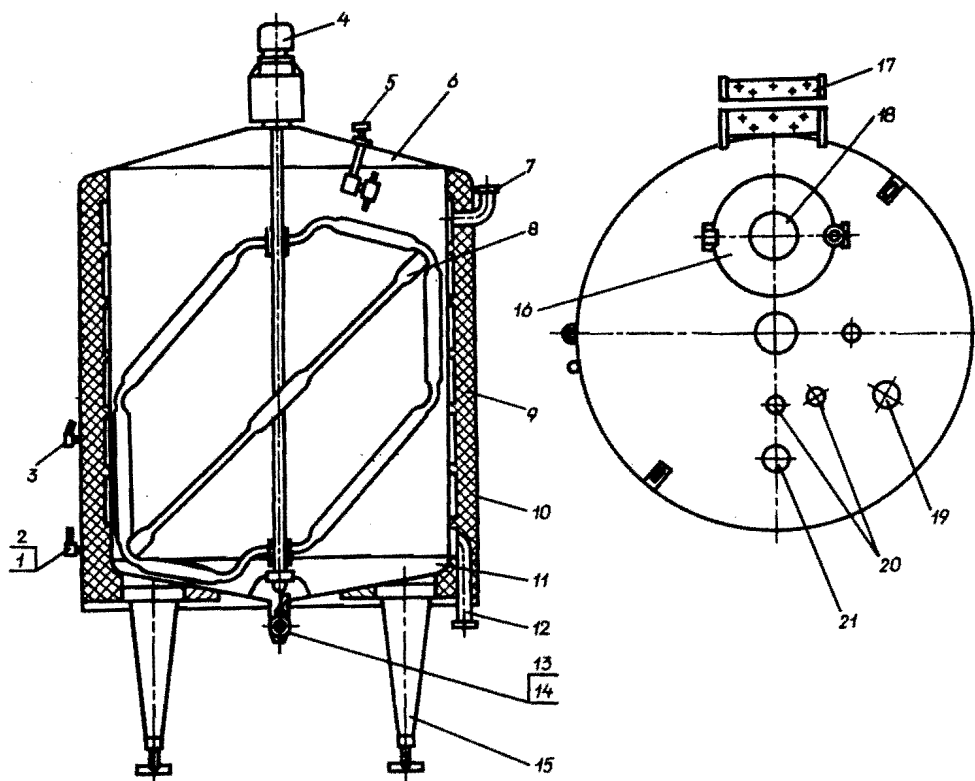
Общий вид резервуара типа Я1-ОСВ:
